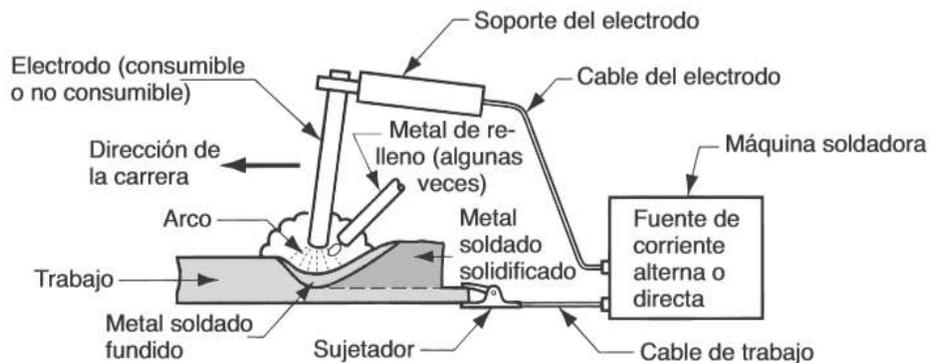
Configuración básica y circuito eléctrico de un proceso de soldadura con arco
